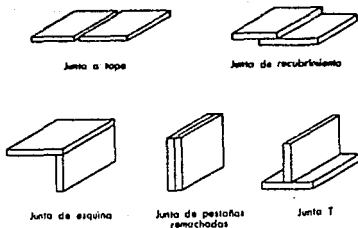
Juntas más comunes en soldadura.
